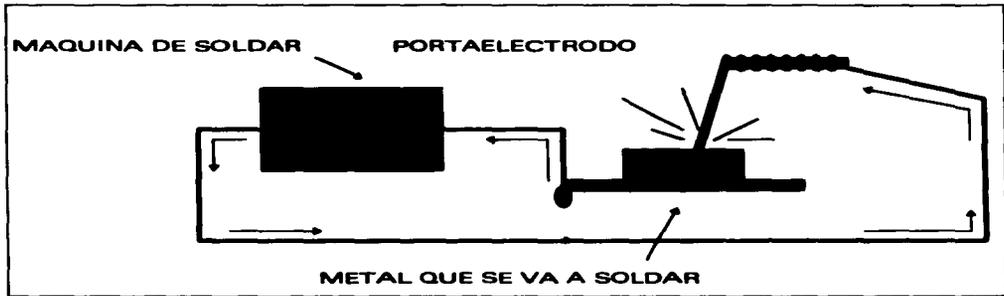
EL CIRCUITO DE SOLDADURA.
